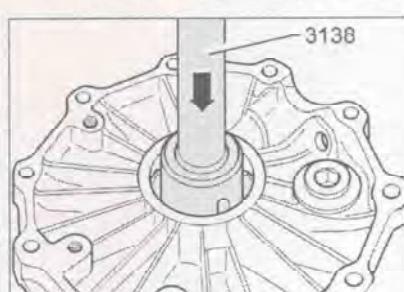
Извлечение наружной обоймы большого роликоподшипника.
